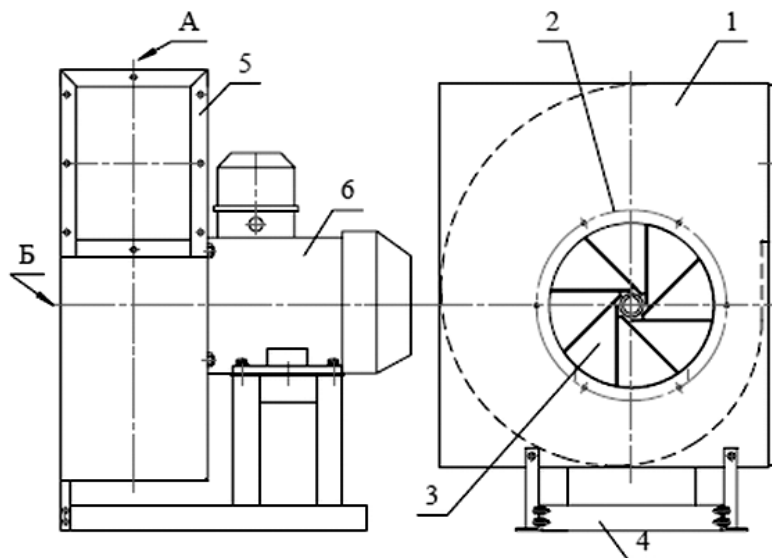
Вентиляторы ВРП-100-57-4. Конструкция и состав.
